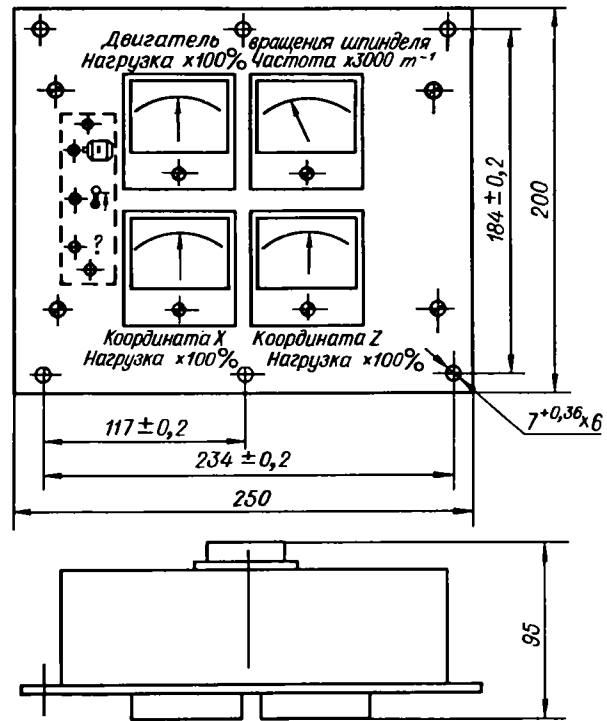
Габаритные и установочные размеры приборного щитка ШПІІ
